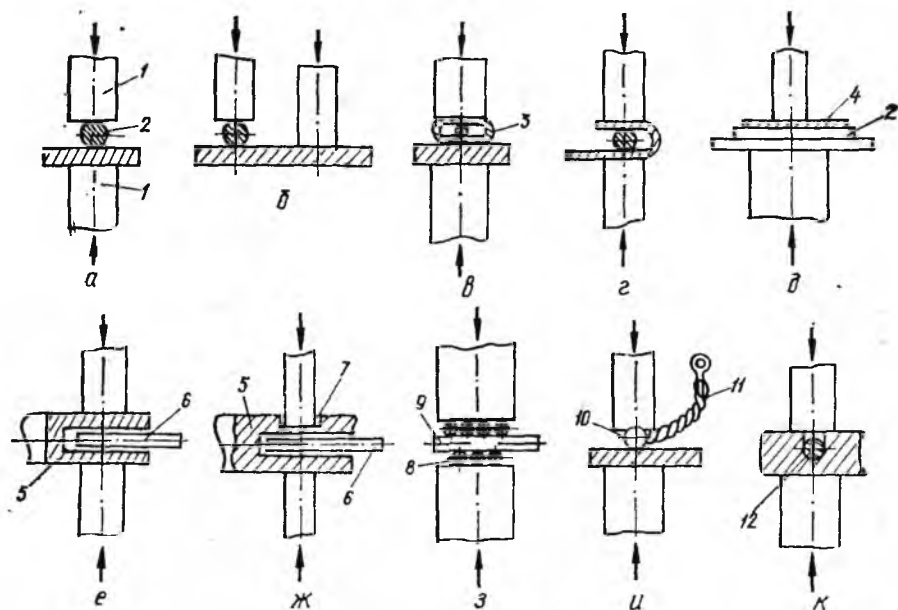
Схемы точечной конденсаторной сварки тонких проводов.
